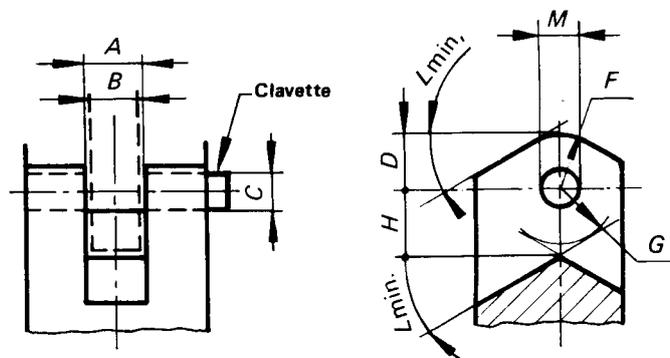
Chape d'extrémité mobile – Encombrement
